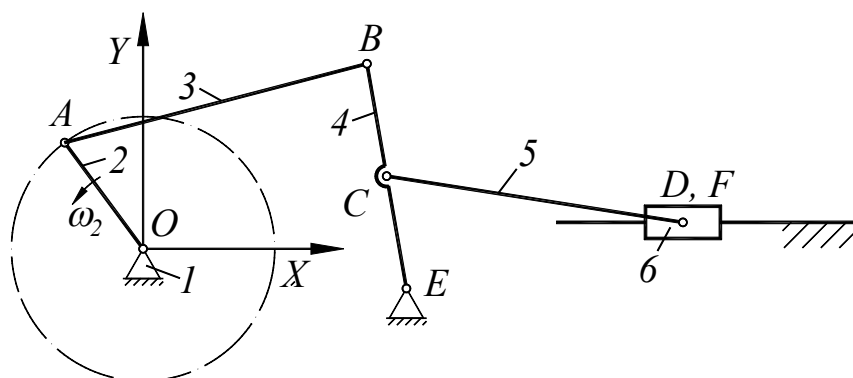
Кинематическая схема механизма подачи заготовки
